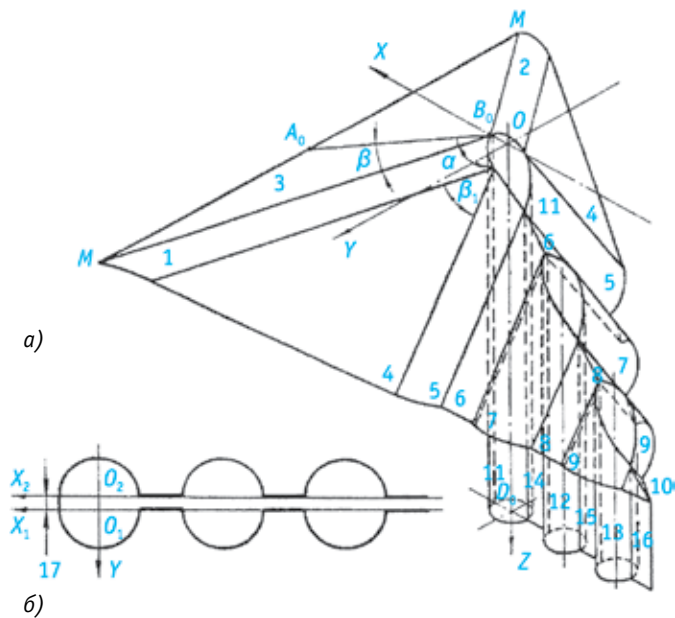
Схема многоручьевого воротникового рукавообразователя: общий вид (а), поперечный разрез цилиндрической части (б)
